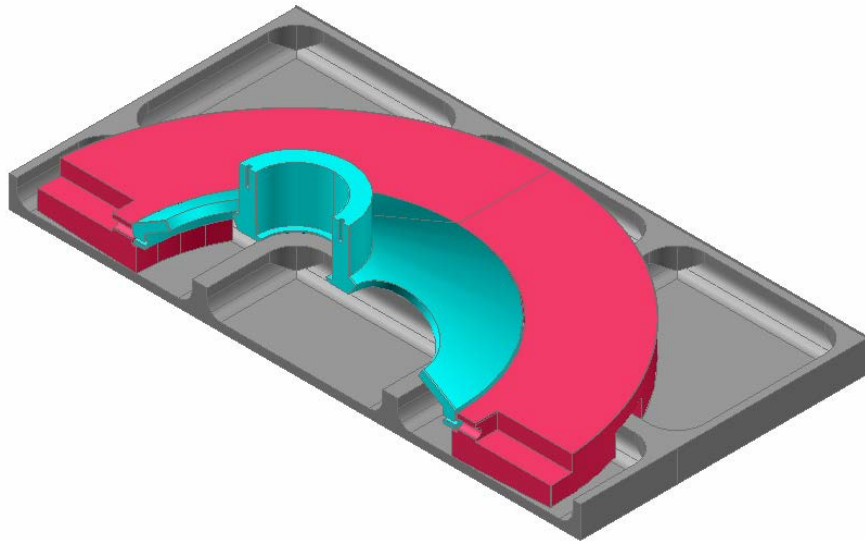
Корпус модуля и бленда на стенке топливного бака.
